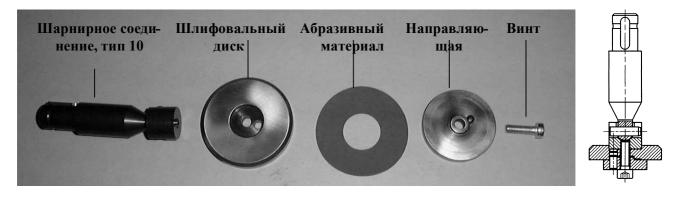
Компоненты инструмента для работы в режиме "ручного станка" с шаровым соединением типа 10 (твердые шлифовальные диски с направляющими)
